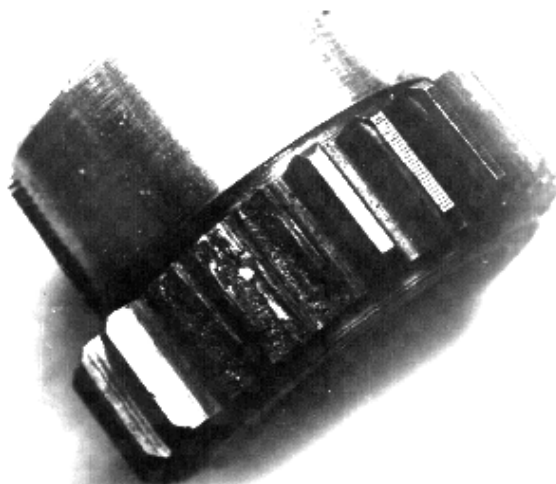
Шестерня токарного станка изготовленная из стали 40X.
